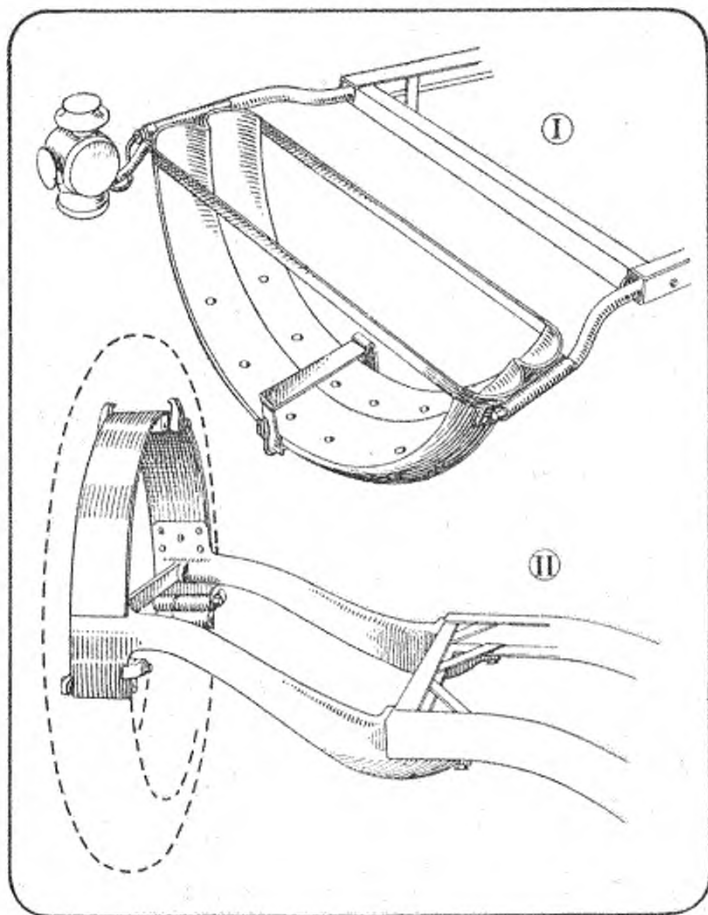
Ferrure avec cuvette ou fausse jante (trop de porte-à-faux).
